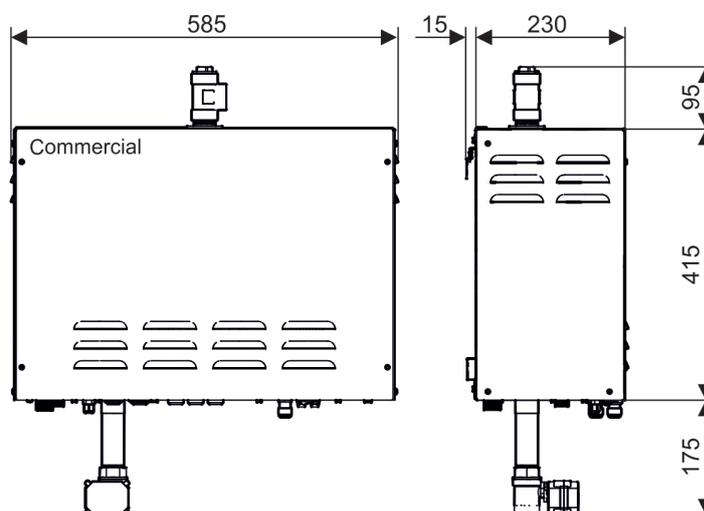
Mått i millimeter, Tylö Ånggeneratorer typ Commercial
